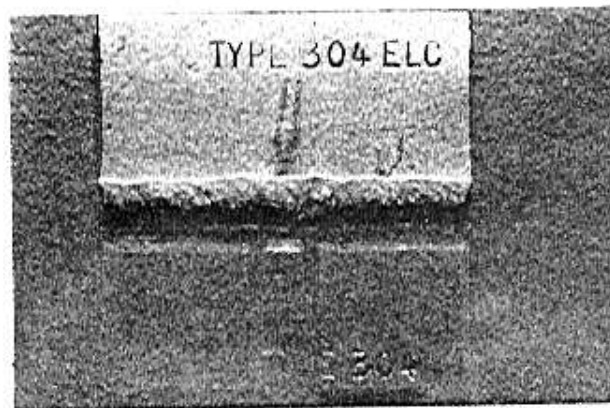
Eliminación de soldadura carcomida por tipos.
